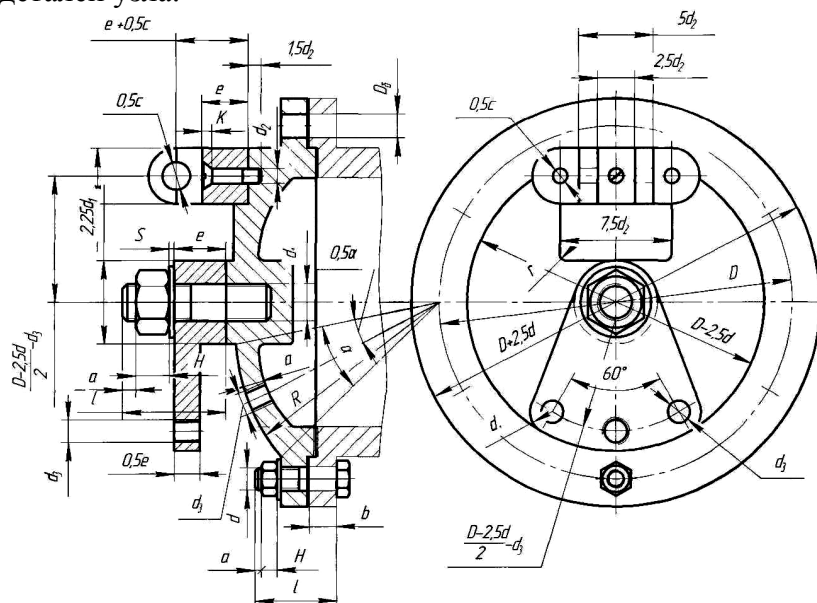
Сборочный чертеж «Крышка тормозного цилиндра»
